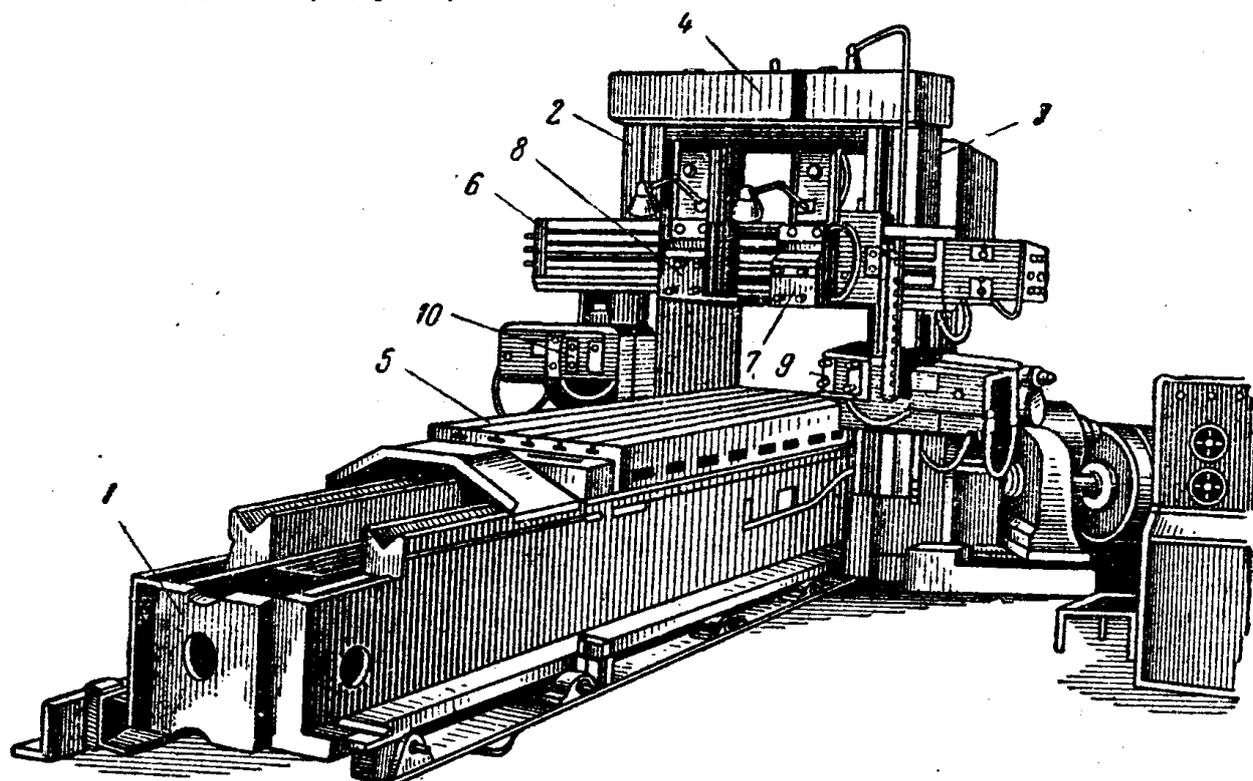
Общий вид продольно-строгального станка модели 7231А: 1 – станина; 2, 3 – вертикальные стойки; 4 – поперечина; 5 – стол; 6 – траверса; 7, 8, 9, 10 – суппорты
